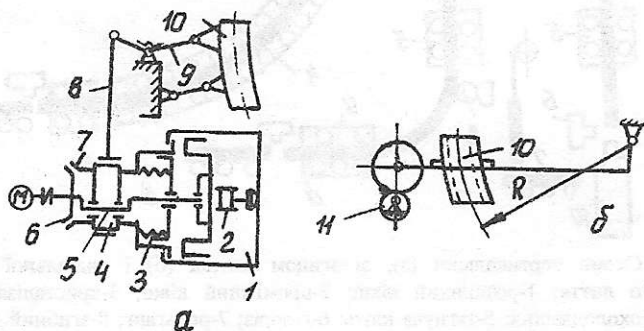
Схеми механізмів качання кристалізатора: 1-траверса; 2-гідроциліндр; 3-пружини; 4-ексцентрик; 5-ексцентриковий вал; 6-напівмуфта; 7-фрикційна муфта; 8-шатуни; 9-чотириланковий механізм; 10-кристалізатор; 11-кулачок
